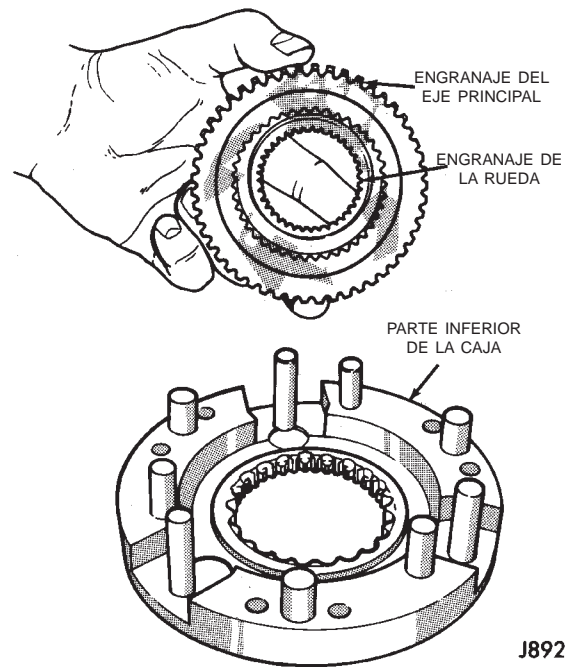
Desmontaje de eje principal y engranaje de la rueda
